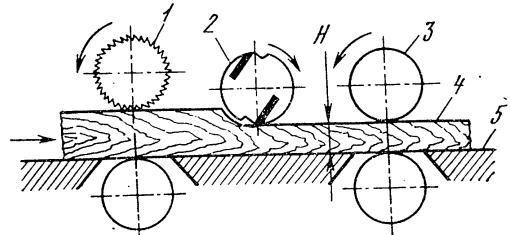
Схема обработки заготовки на рейсмусовом станке:
